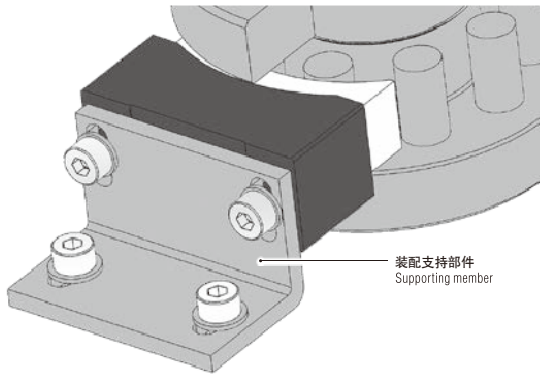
TLS 装配相关 Fig. 1 — Mounting TLS —
